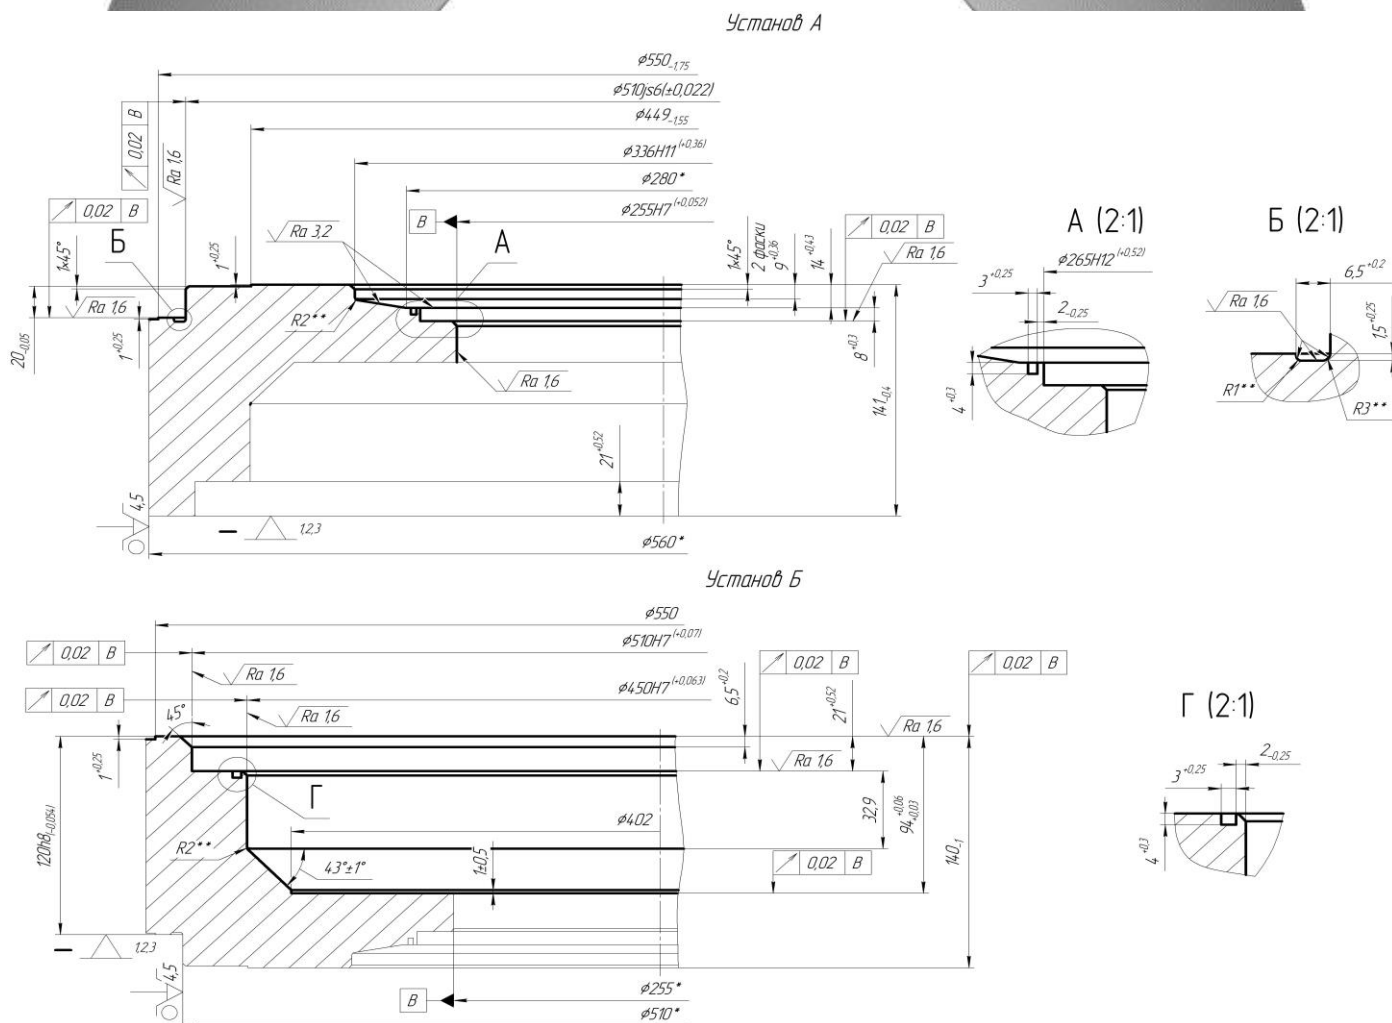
Схема базування заготовки на токарній операції (другий варіант)
